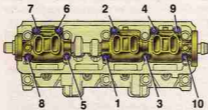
Порядок затягивания гаек крепления корпусов подшипников распределительного вала
